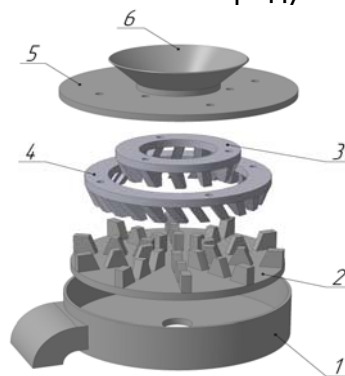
Измельчитель центробежно-роторного действия: 1 – корпус; 2 – нижний диск-ротор; 3, 4 – кольца первой и второй ступеней измельчения; 5 – крышка; 6 – приёмная камера
